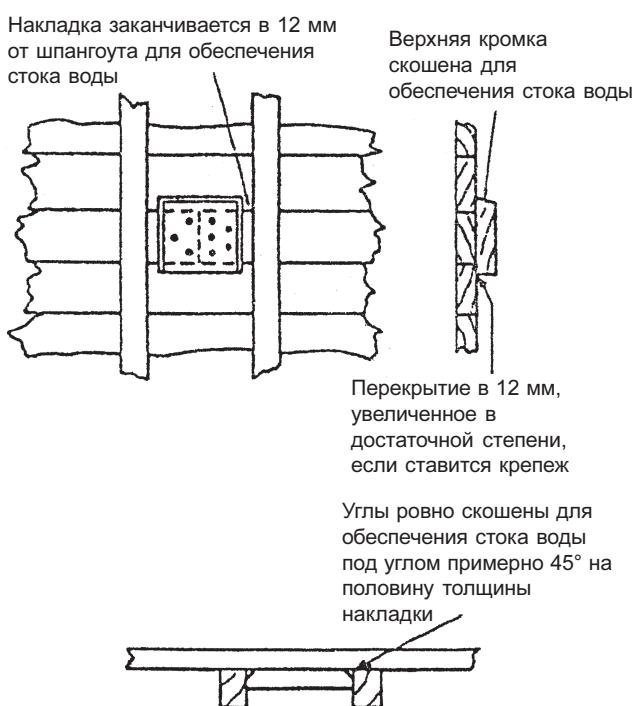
Типовые стыковые накладки для однослойной обшивки корпуса
